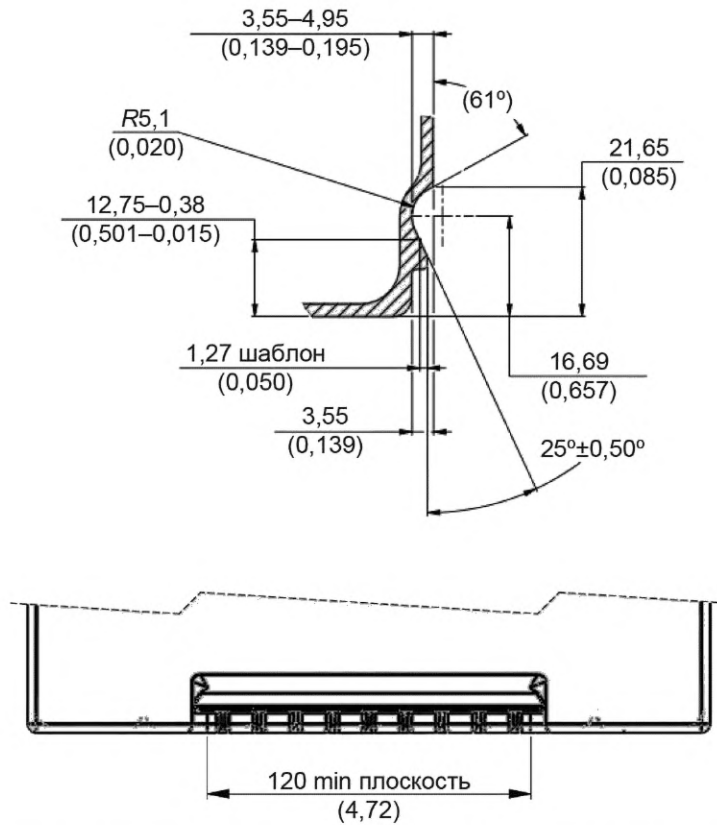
Форма и размеры углублений на корпусе, образующих бортик на длинной стороне батареи
